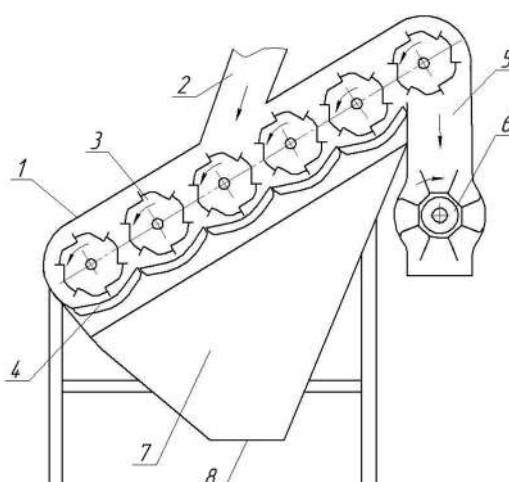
Схема лабораторного стенда нового сепаратора-очистителя.
